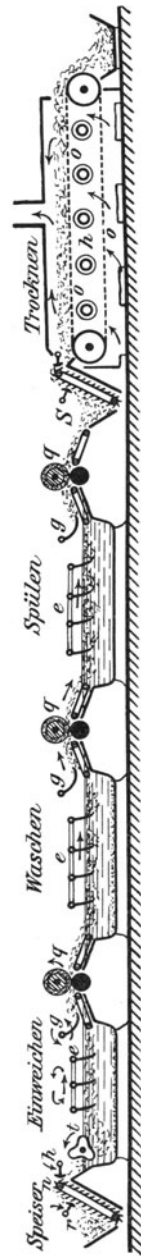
Selbsttätige Wollwasch- und Trockenmaschine.
